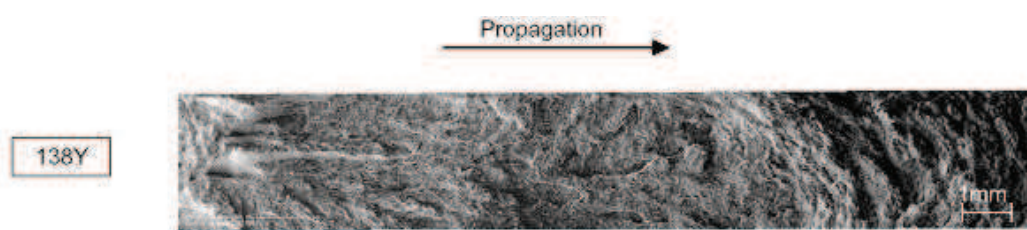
Fractographies des propagations de fissure - éprouvettes CT testées à -50°C
